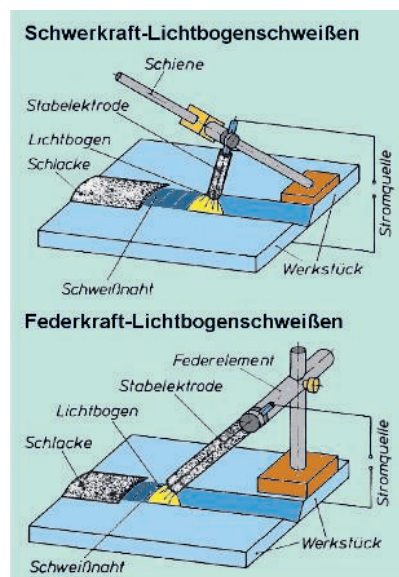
Nicht mehr im Einsatz: Schwer- und Federkraft-Lichtbogenschweißen.
